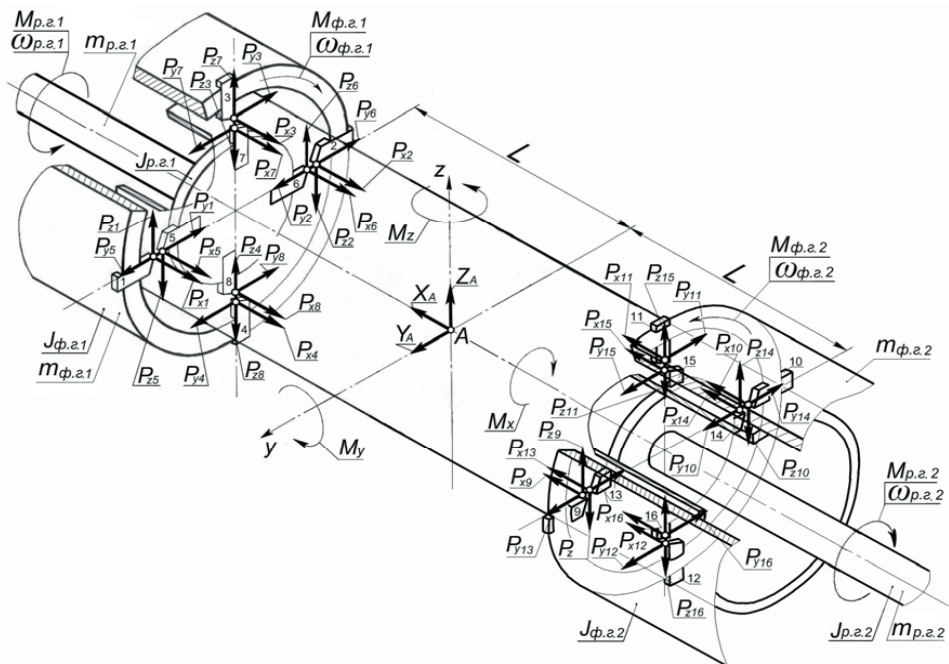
Розрахункова схема роботи пристрою для обробки кінців труб
